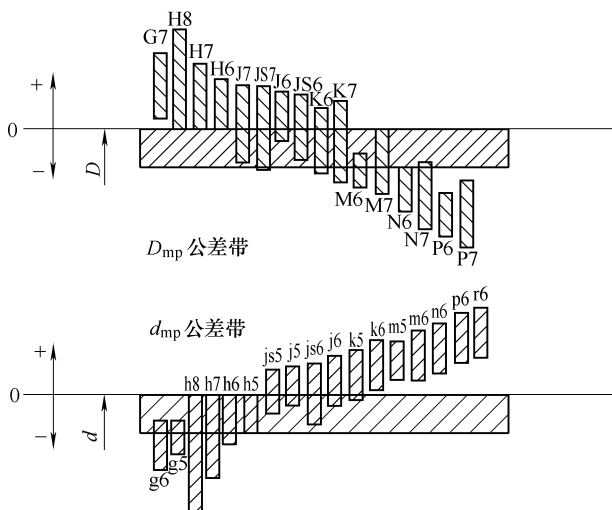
滚动轴承与轴和壳体孔的公差与配合
